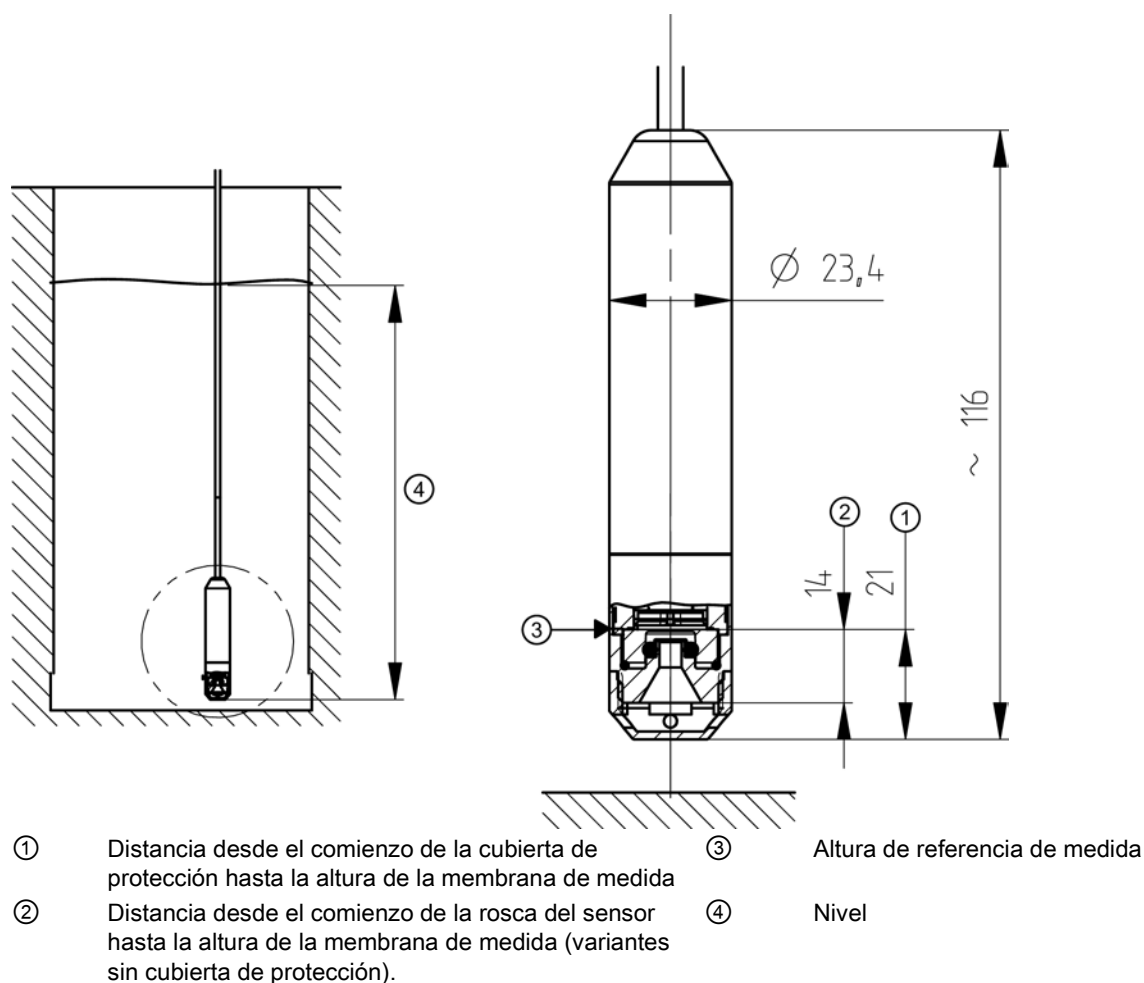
Montaje del transmisor de presión, dimensiones en mm
